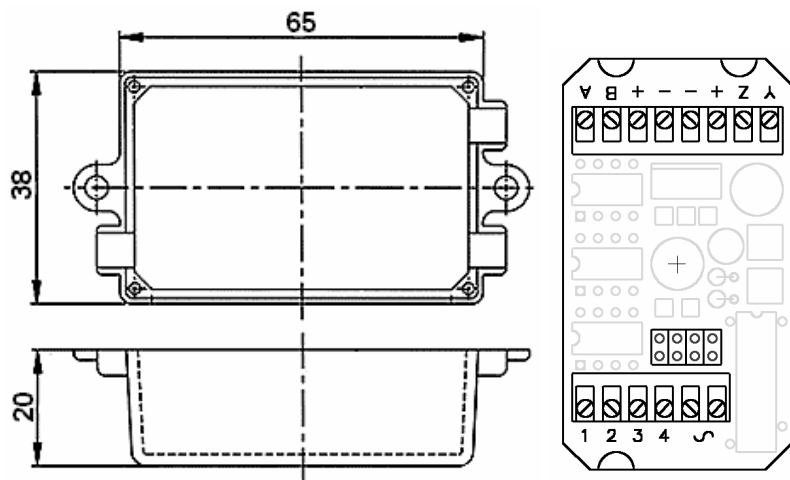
Корпус и печатная плата датчика Smart-Alarm.
